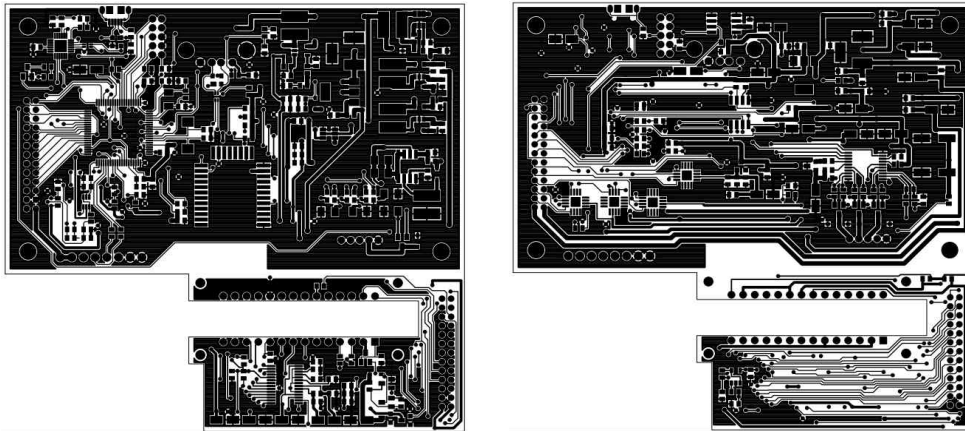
Top(좌) & Bottom(우) 회로도에 대한 Drawing 이미지
